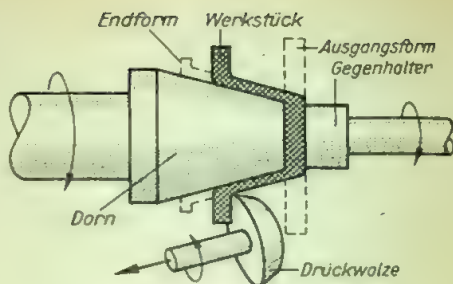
Projizierdrückwalzen (-streckdrücken)
